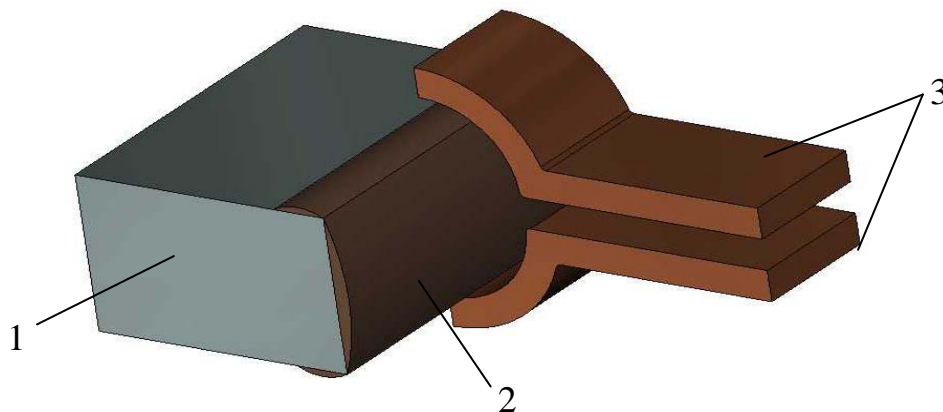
Схема дифузійного борування з паст і обмазок при нагріванні СВЧ плоских деталей: 1 – зміцнювальна деталь; 2 – обмазка; 3 – індуктор
